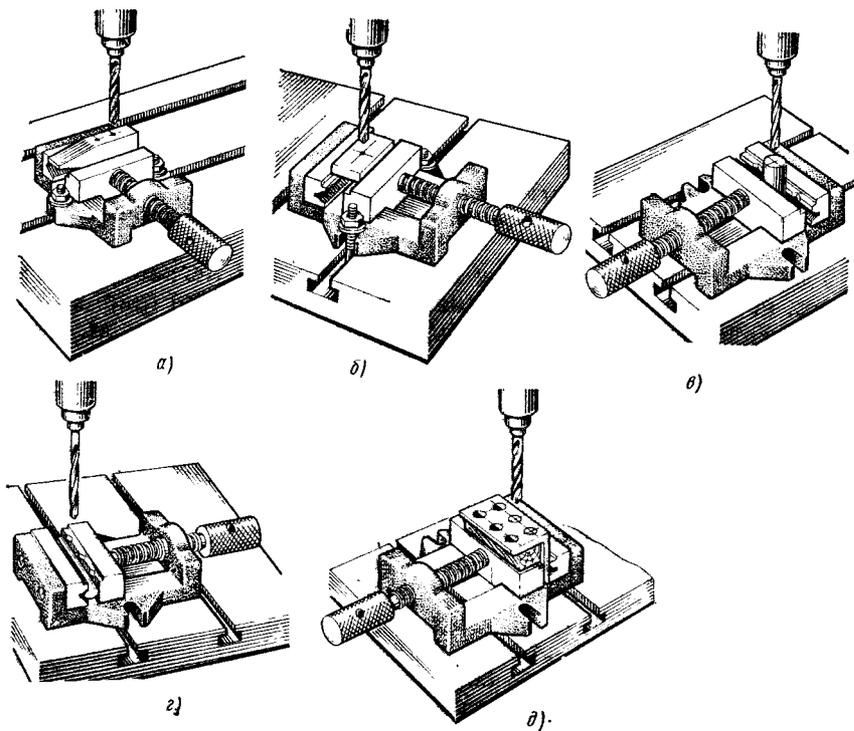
Крепление в машинных тисках с призматическими губками деталей различной формы:
